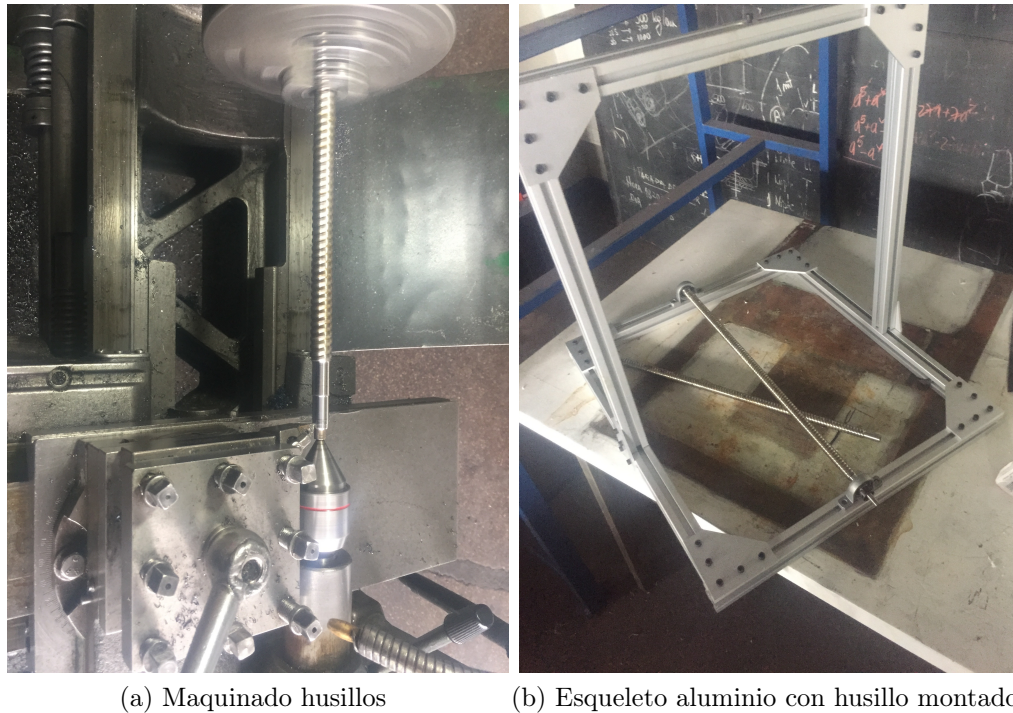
Maquinado y montaje husillo. Fuente Elaboracion propia
